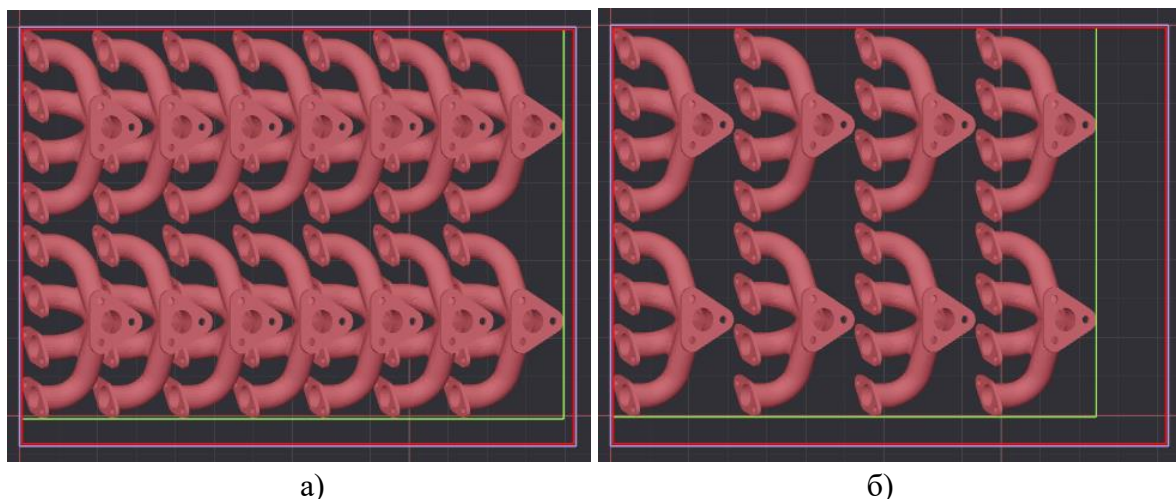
Влияние параметра «Перекрытие»: а) результат, когда перекрытие было разрешено (вид сверху); б) результат, когда перекрытие было запрещено (вид сверху)
